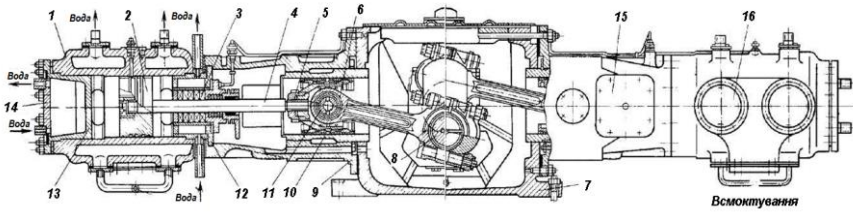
Ополитний компресор АТ-600П: 1 – циліндр; 2 – поршень; 3 – сальник поршневого штока; 4 – шток поршневий; 5 – крейцкопф (ковзна опора); 6 – шатун; 7 – рама; 8 – колінвал; 9 – корпус напрямної крейцкопфа; 10 – напрямна крейцкопфа; 11 – палець; 12 – кришка циліндра; 13 – глуха кришка; 14 – кришка водяної порожнини; 15 – корінні підшипники; 16 – механізм повертання колінвала
